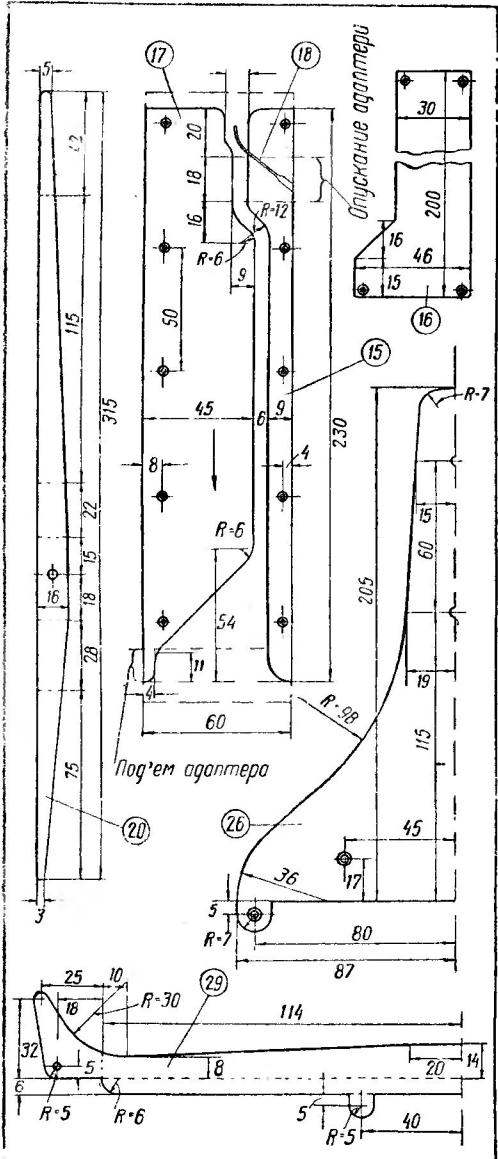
Крупные детали автомата, изготовленные из листового металла
